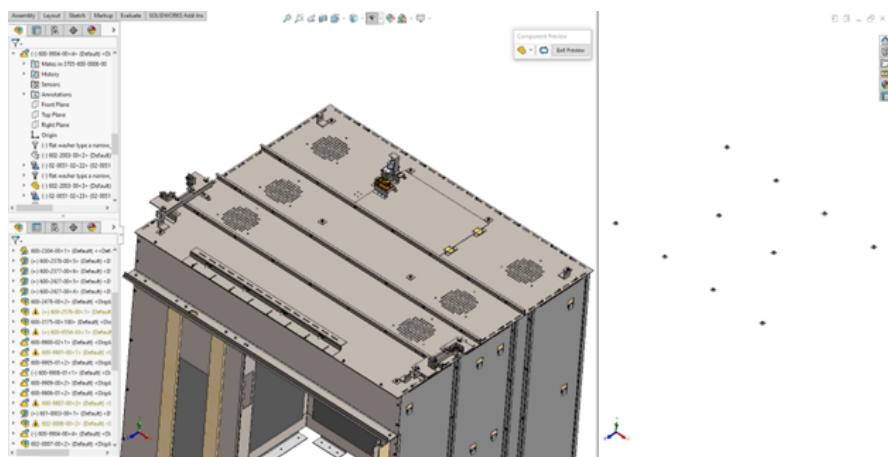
También se puede utilizar en el subensamble de los bolt packs para seleccionar cada uno sin problema
